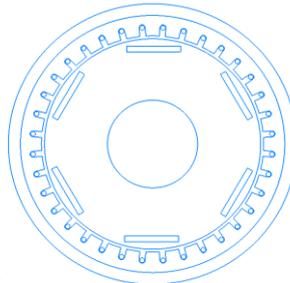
Общий вид электродвигателя с неодимовыми магнитами. Fig. 3. The general appearance of an electric motor with neodymium magnets.
